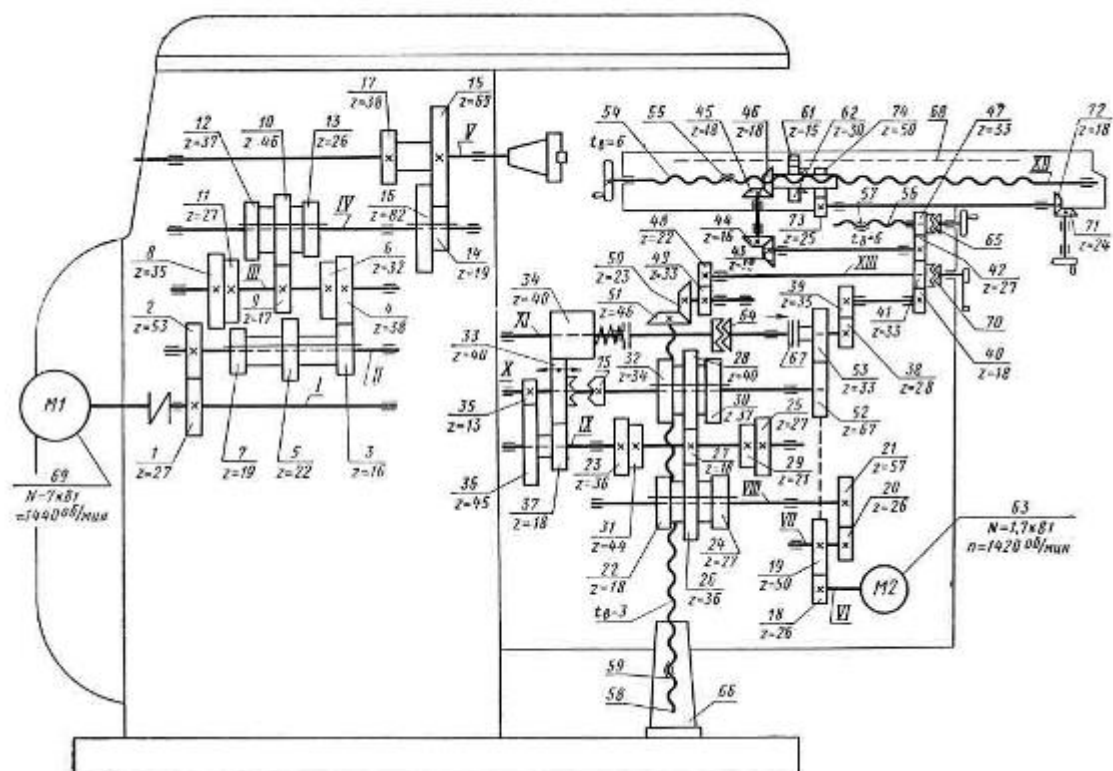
Кинематическая схема горизонтально-фрезерного станка 6М82
